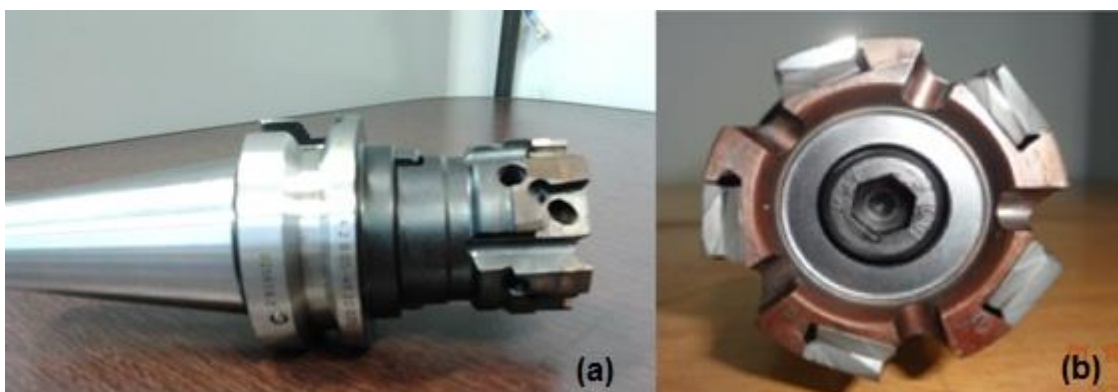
Fresa frontal: (a) fresa com o cone; (b) fresa com os inserts
